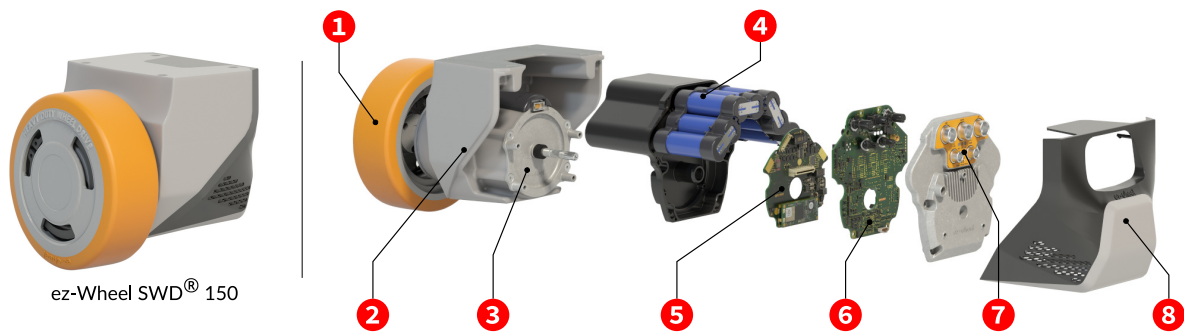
La SWD® 150 d’ez-Wheel illustrée avec la roue assemblée à gauche et une vue éclatée sur les composants internes à droite. (1) Roue et train d’engrenages épicycloïdal, (2) Boîtier en acier dimensionné pour supporter des fortes charges, (3) Moteur BLDC, (4) Bloc de batteries, (5) Système de gestion de batterie (BMS) et optionnellement un SoM DART-MX6 avec un processeur NXP/Freescale i.MX6 Quad-core Cortex-A9™, (6) Codeur à effet Hall, électronique de contrôle sûr et de communication, (7) Prises de connectivité, (8) Boîtier en plastique.
